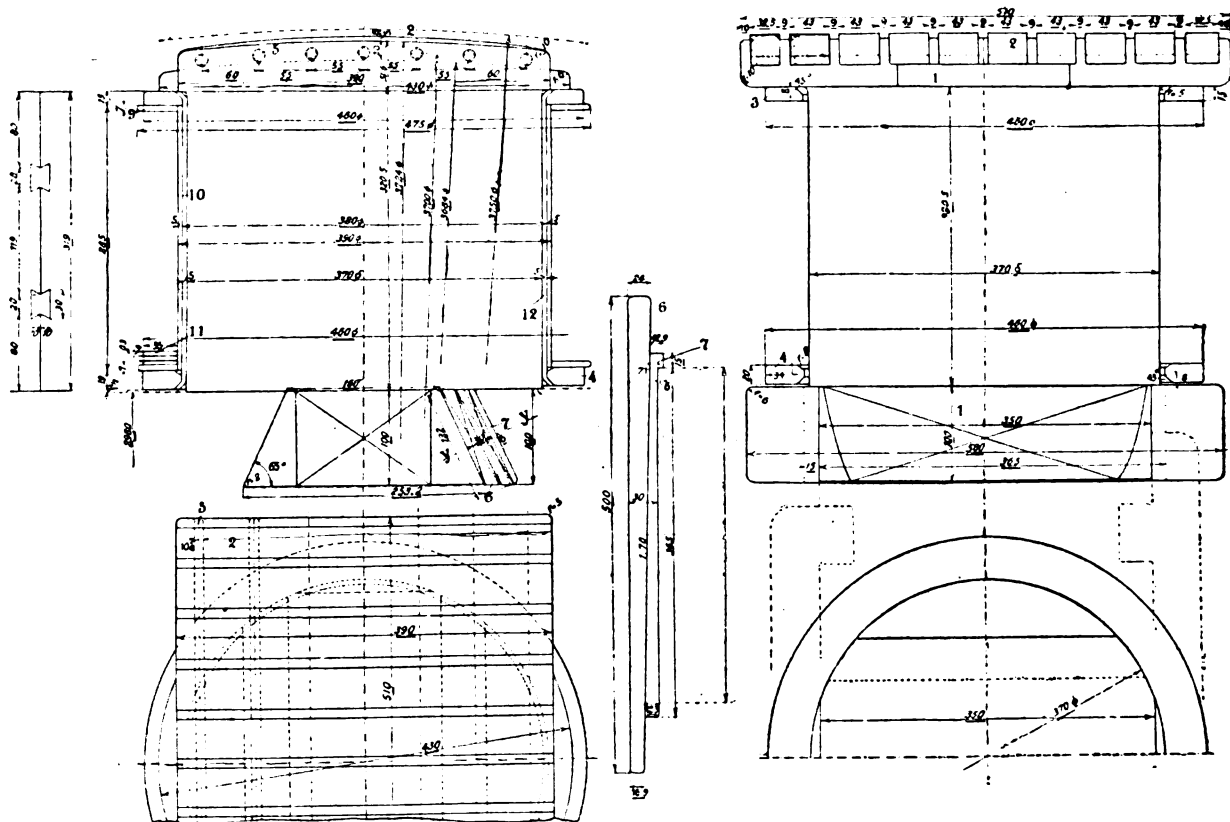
Mode de construction des pôles, vue et coupe en plan et en élévation.
